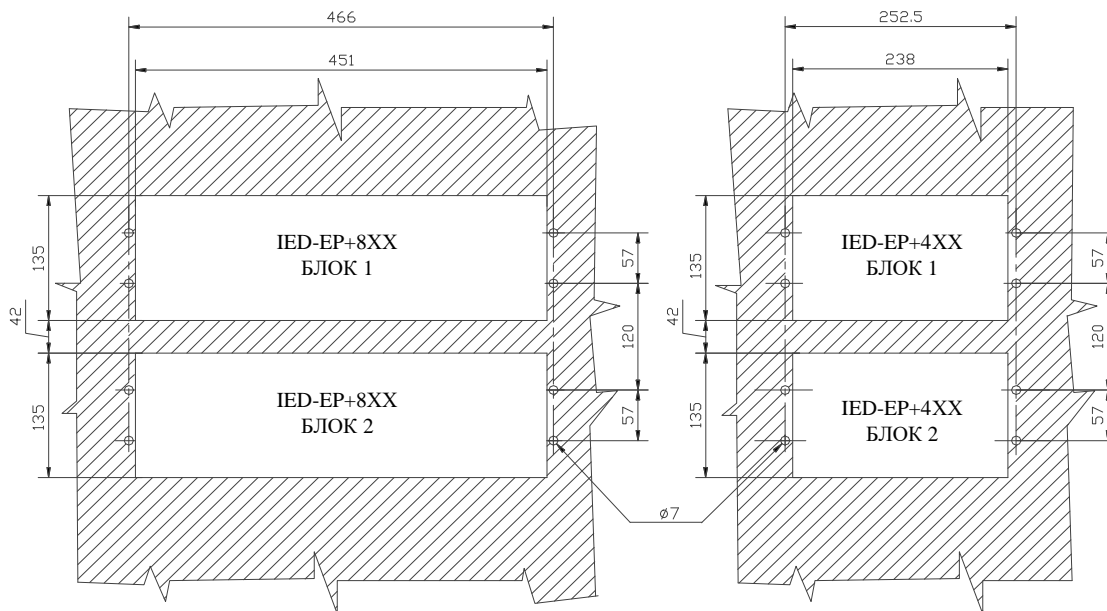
Габаритные, установочные и присоединительные размеры модификаций IED-EP+8XX и IED-EP+4XX и разметка для монтажа в шкаф
